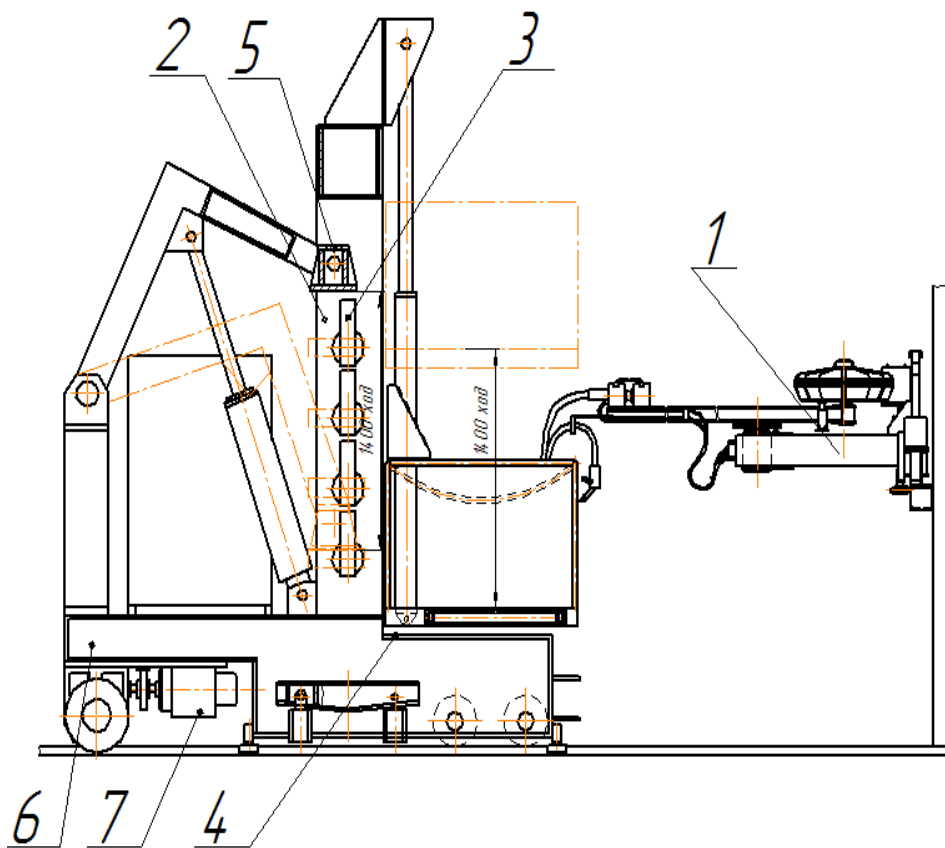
Специализированный стенд для сборки и сварки балки концевой:
